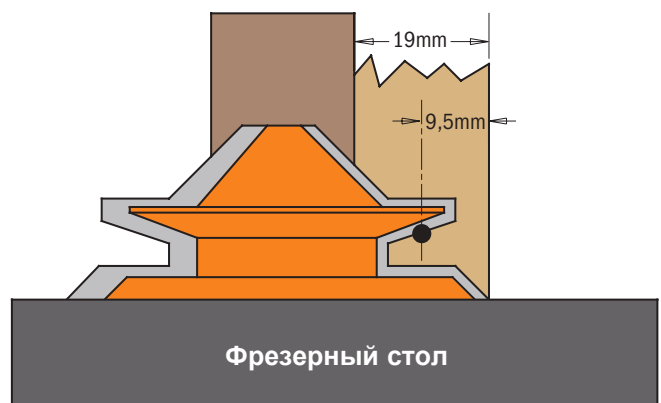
Отфрезеруйте вторую деталь внутренней стороной к упору.
